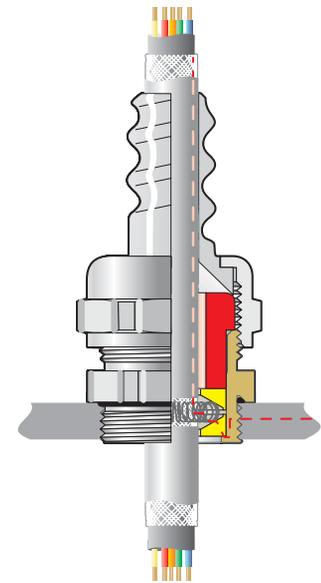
UNI HF-UL Dicht mit Schlauch montiert
